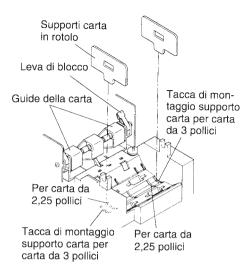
Montaggio dei supporti carta in rotolo (SP342)
